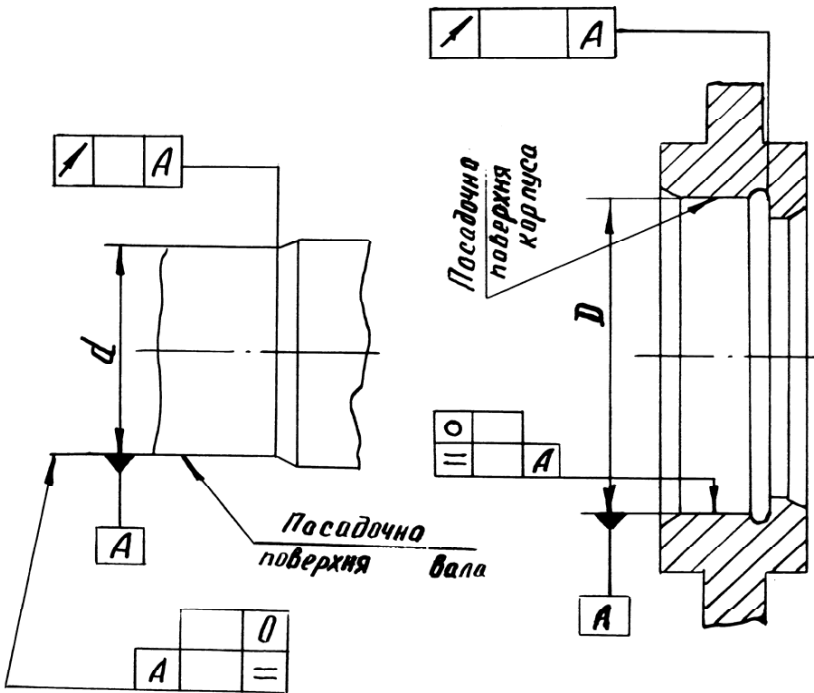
Позначення допусків форми і положення опорних торцевих поверхонь заплечиків вала і корпусу.
